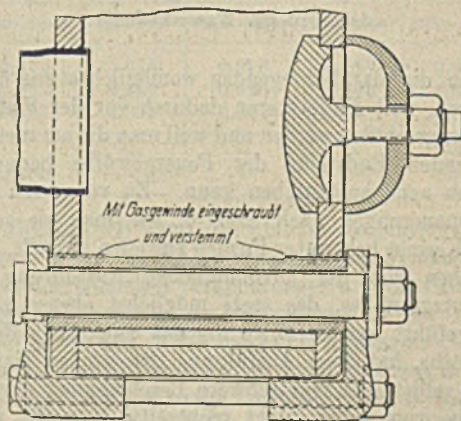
Vorrichtung zur Sicherung der Schweißnähte von Wasserkammern.
